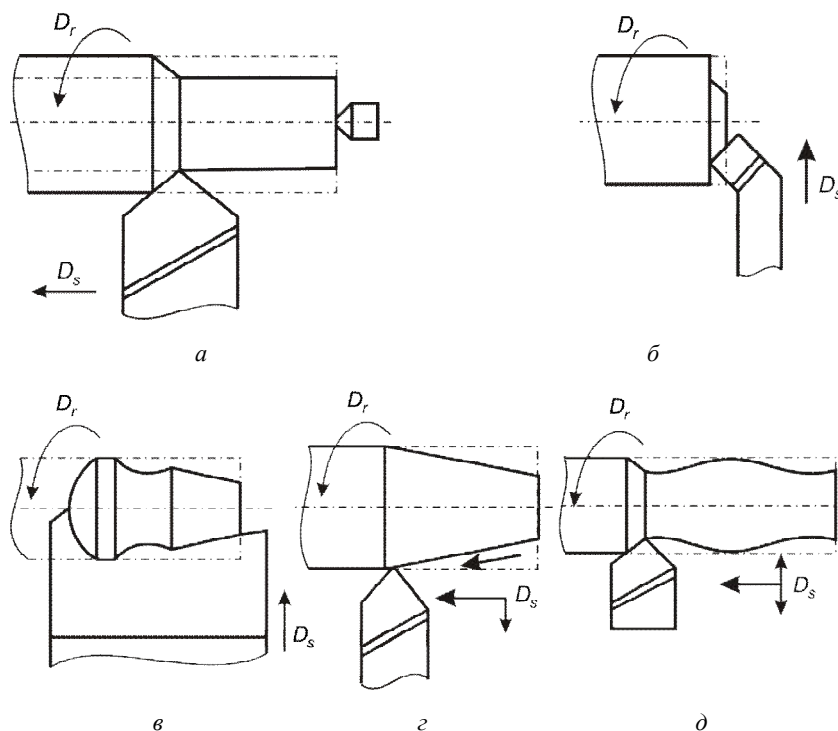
Главные движения резания и движения подачи при обработке различных поверхностей деталей точением: а – цилиндрической; б – торцевой; в, г – фасонной; з – конической
